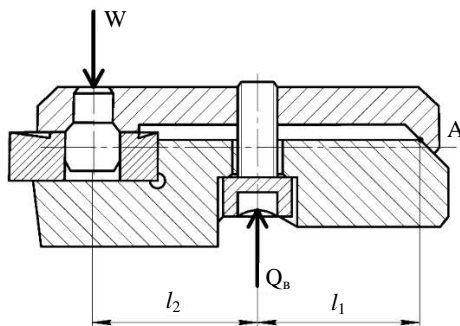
Расчётная схема рычажного механизма в резцовом блоке
